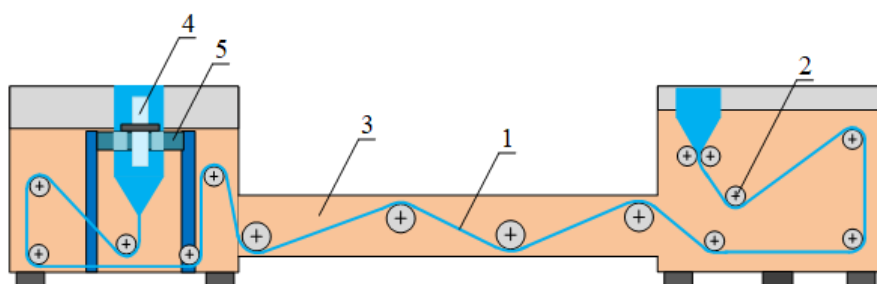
Зона термостатирования заготовки: 1 – пленка; 2 – тянущие валы; 3 – резервуар с водой; 4 – узел подачи воздуха; 5 – охлаждающее кольцо
